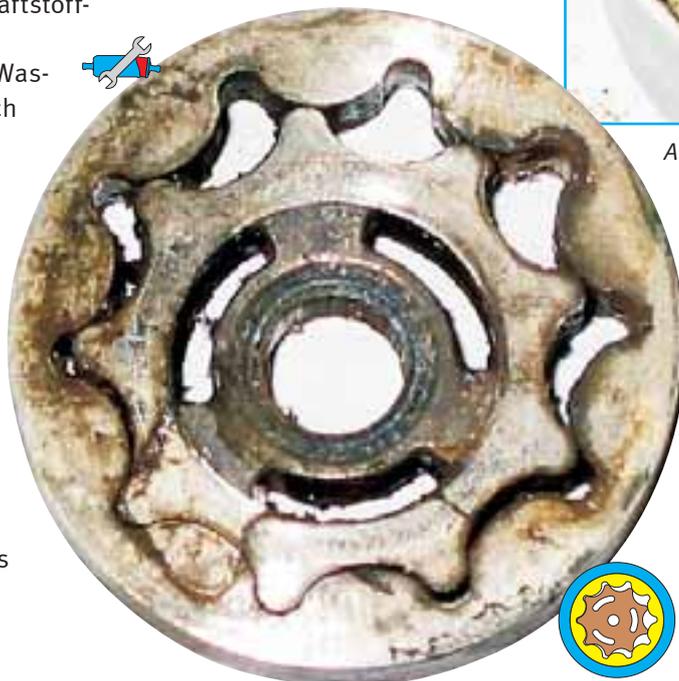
Blockiertes Pumpenwerk (Trochoiden-Zahnring) einer Zahnringpumpe E3T
